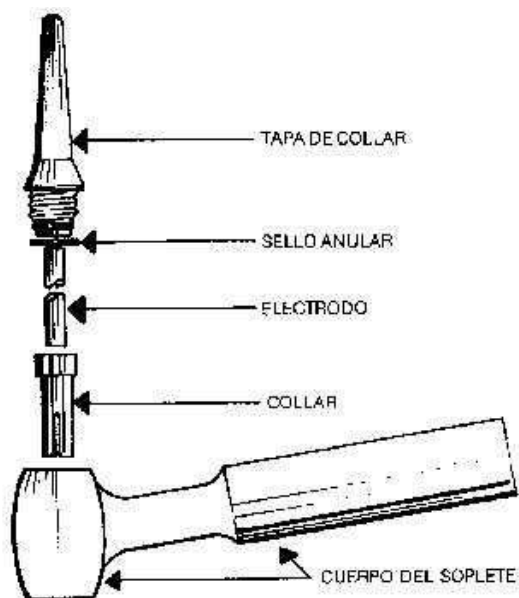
Partes de una antorcha para soldadura de proceso GTAW⁴²
